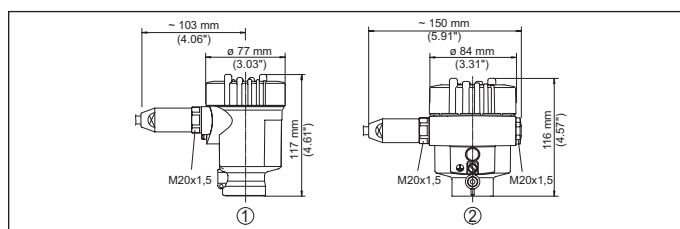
Исполнения корпуса со степенью защиты IP 66/IP 68 (1 bar) для VEGASWING 61, 63, 66
